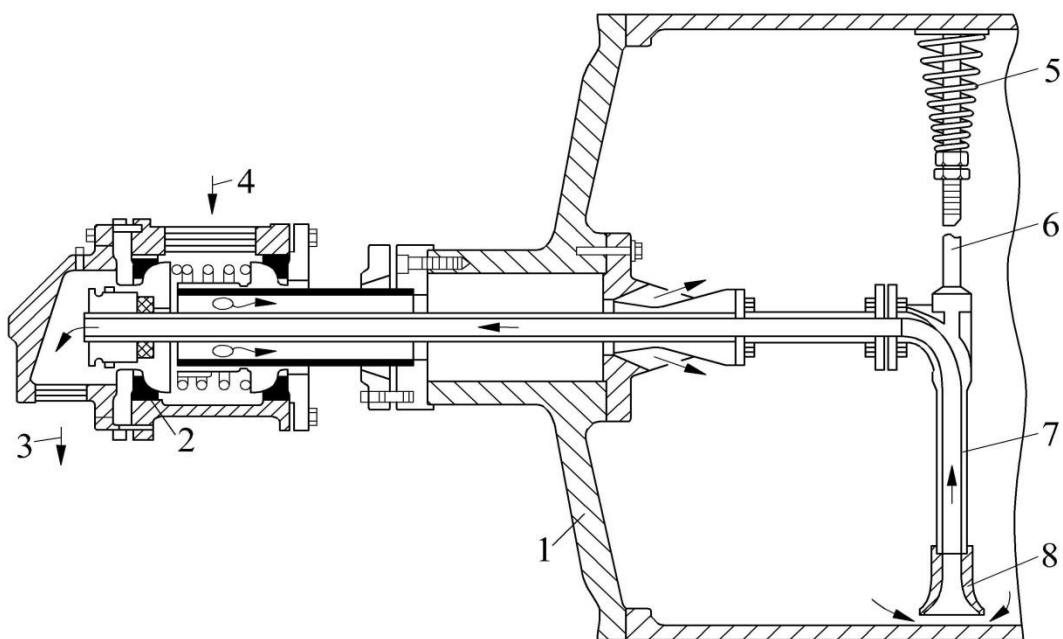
Вращающийся сифон и паровая головка сушильного цилиндра:
